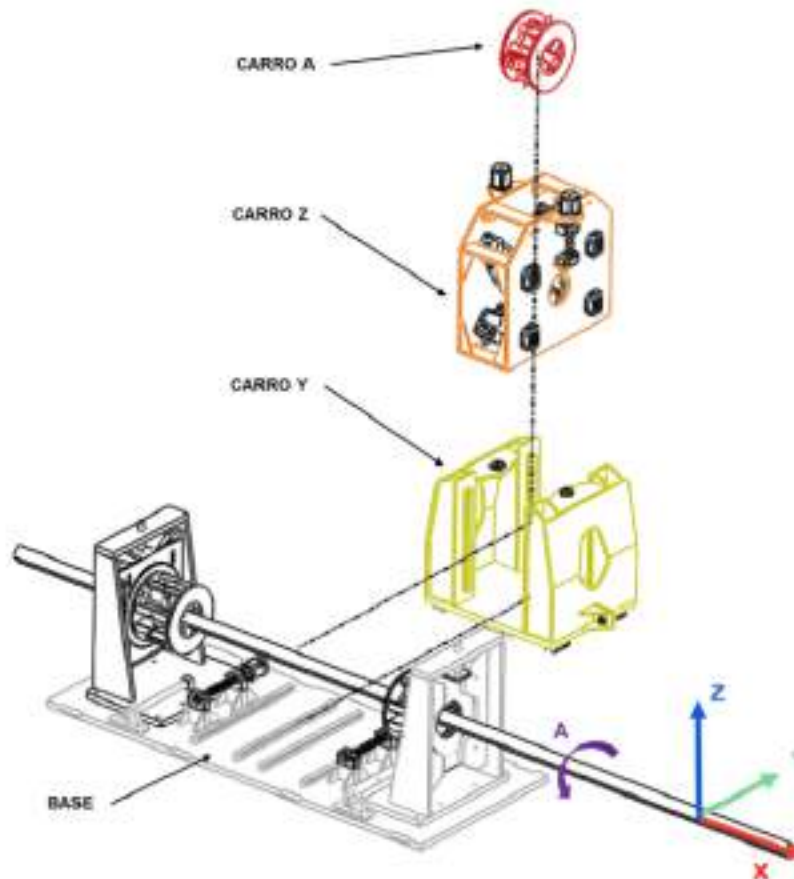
Vista isométrica del mecanismo completo explosionado.
